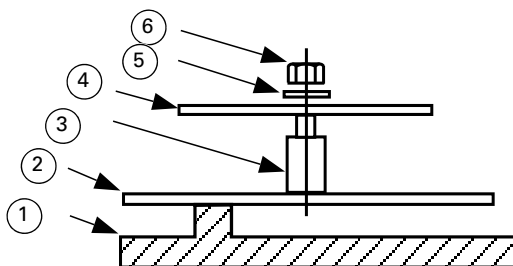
ANC-8, dettaglio del fissaggio dei PCB
